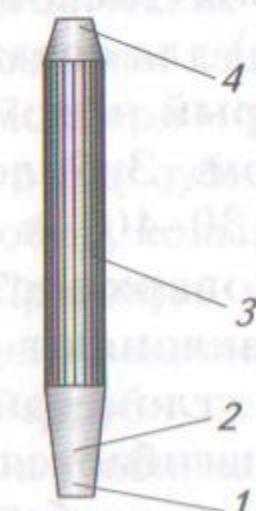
Зубило: 1 — режущая кромка; 2 — боковая поверхность лезвия; 3 — стержень; 4 — ударная часть
